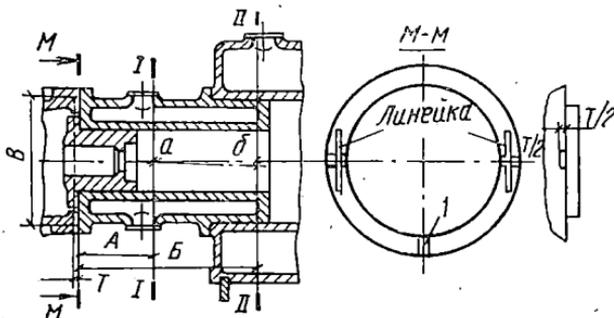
Схема опилки торца цилиндра для устранения излома осей
